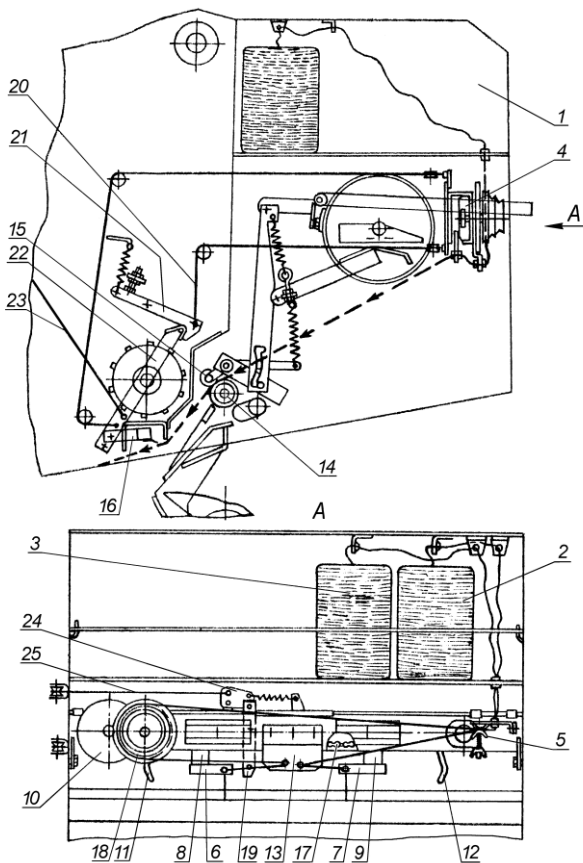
Механизм обмотки рулонов шпагатом: 1 – ящик; 2 и 3 – бабина; 4 – обматывающий аппарат; 5 – тормоз шпагата; 6 и 7 – пководки; 8 и 9 – каретки; 10 – механизм привода кареток; 11 и 12 – ограничители; 13 – кронштейн; 14 – обрезиненный вал; 15 – прижимной ролик; 16 – нож; 17 – цепной контур; 18 – шкив; 19, 22 и 24 – рычаг; 20, 23 и 25 – тяги; 21 – защелка.
